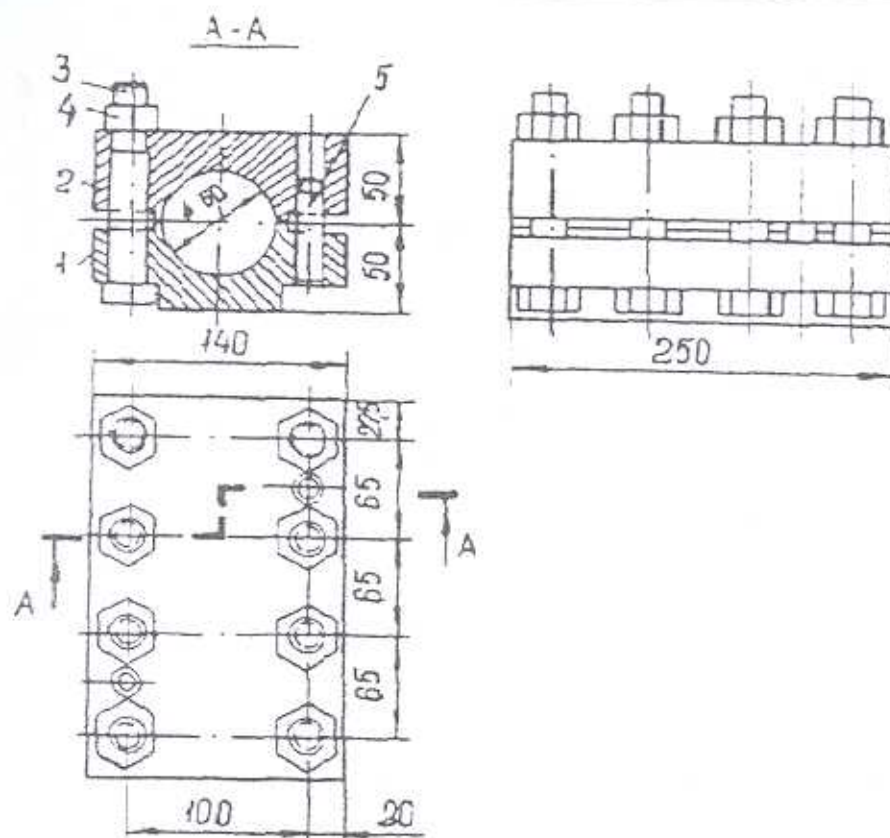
Пресс-форма для опрессовки изоляции токоведущих болтов ротора:
